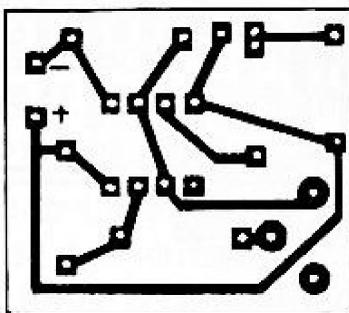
Sugestão, em tamanho natural, para a confecção de uma plaqueta para a montagem do dispositivo.
